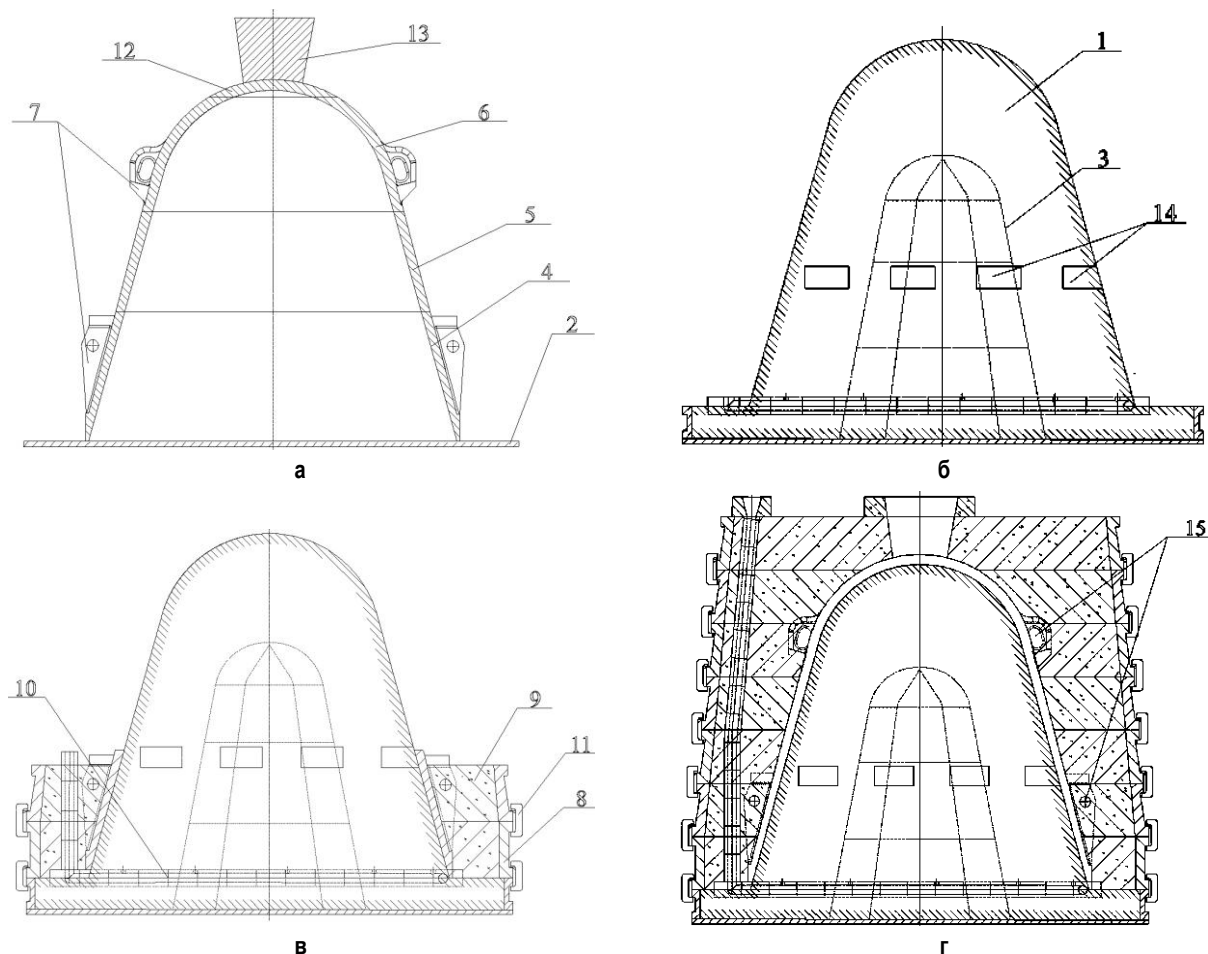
Технология изготовления отливки «Шлаковая чаша»:
